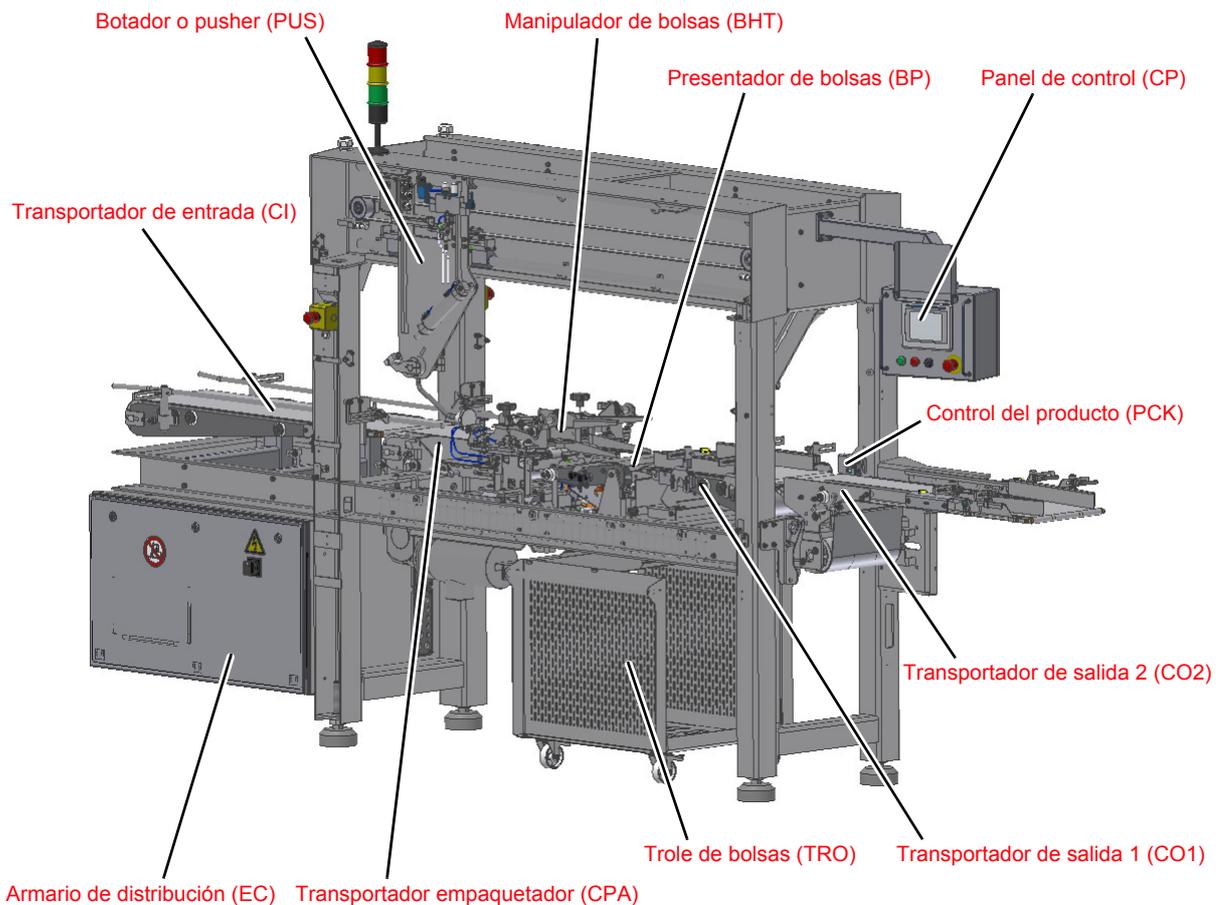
, Elementos principales de la máquina (ilustrados sin protección)
